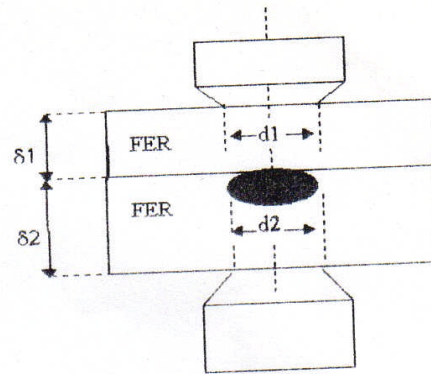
soudage de deux pièces d'épaisseurs différentes,  $d_1=d_2$
